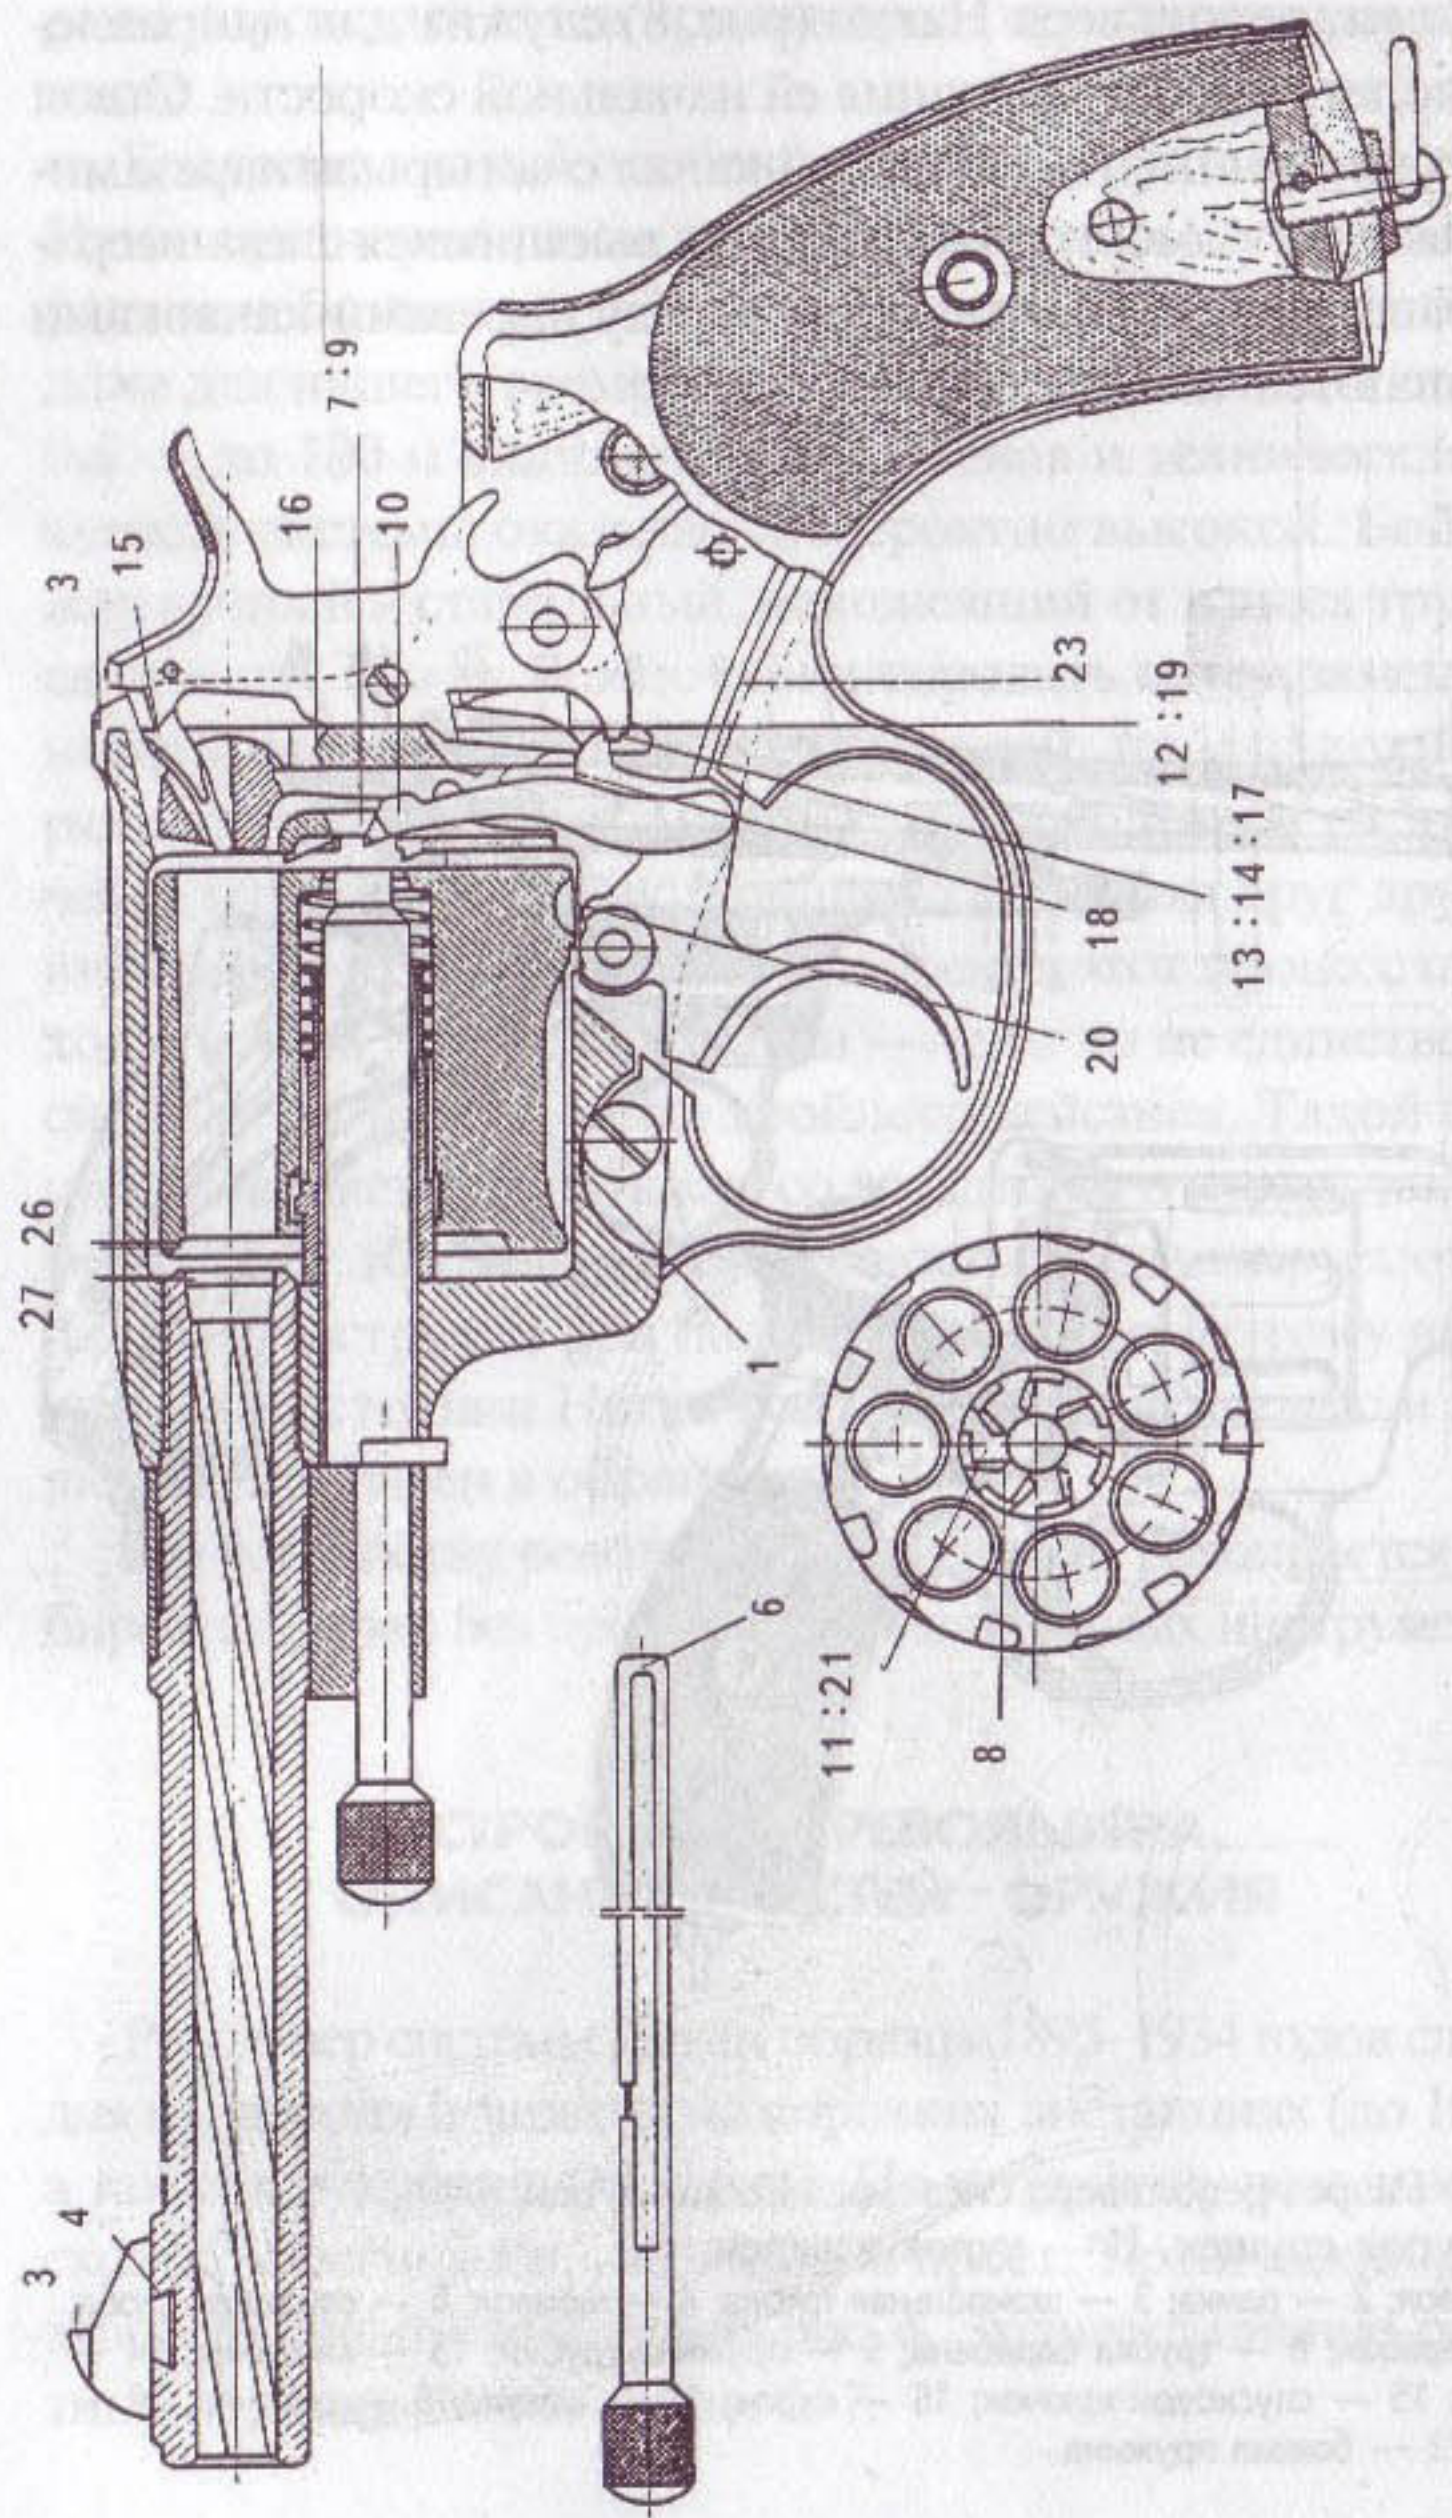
Эксплуатационно-ремонтный чертёж 7,62-мм револьвера системы Наган образца 1895 года, вид слева
